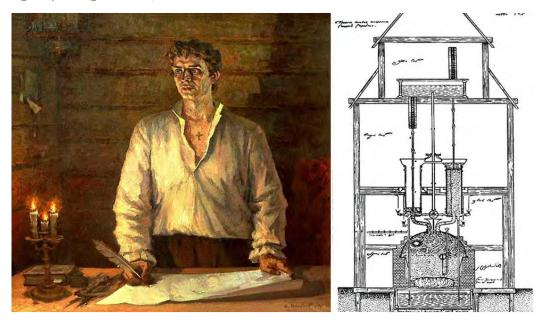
Двухцилиндровый паровой двигатель И. И. Ползунова 66
